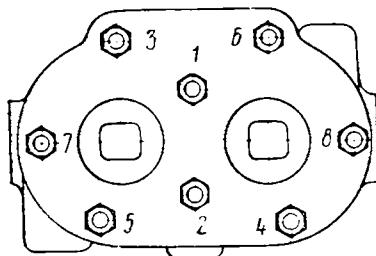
Порядок затягивания гаек шпилек крепления головки цилиндров компрессора
